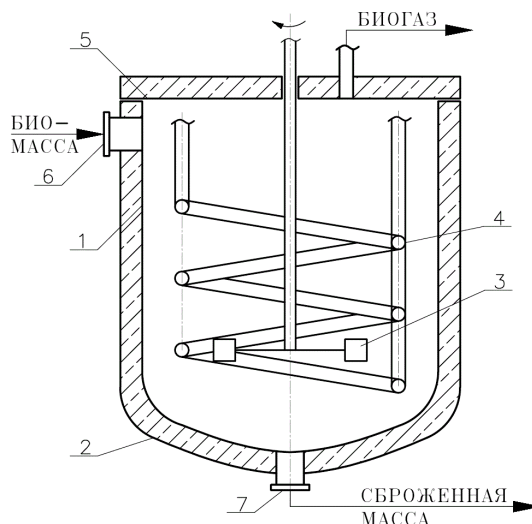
Схема метантенка для фермерского хозяйства:
